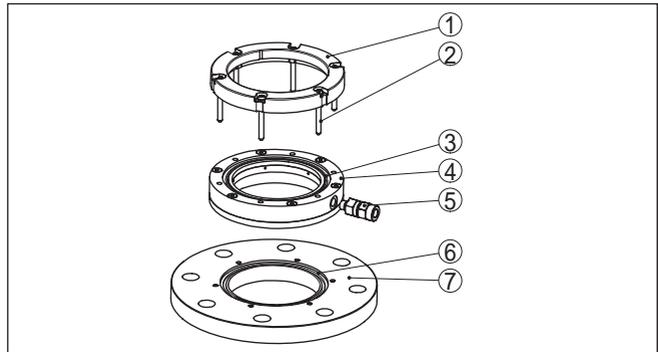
Montagem da conexão de lavagem em flange adaptador
